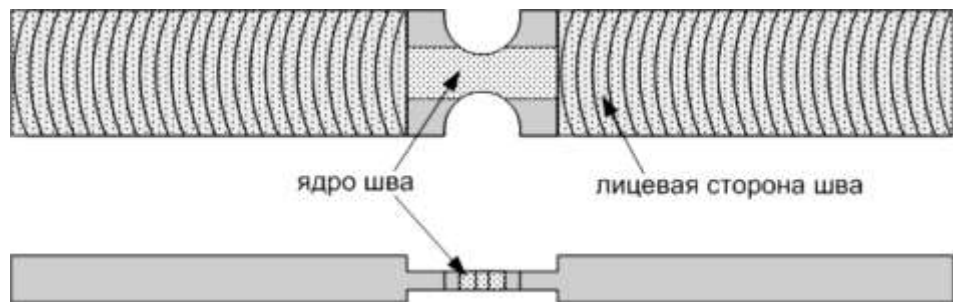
Схема вырезки образцов из ядра сварного шва для испытаний на растяжение
